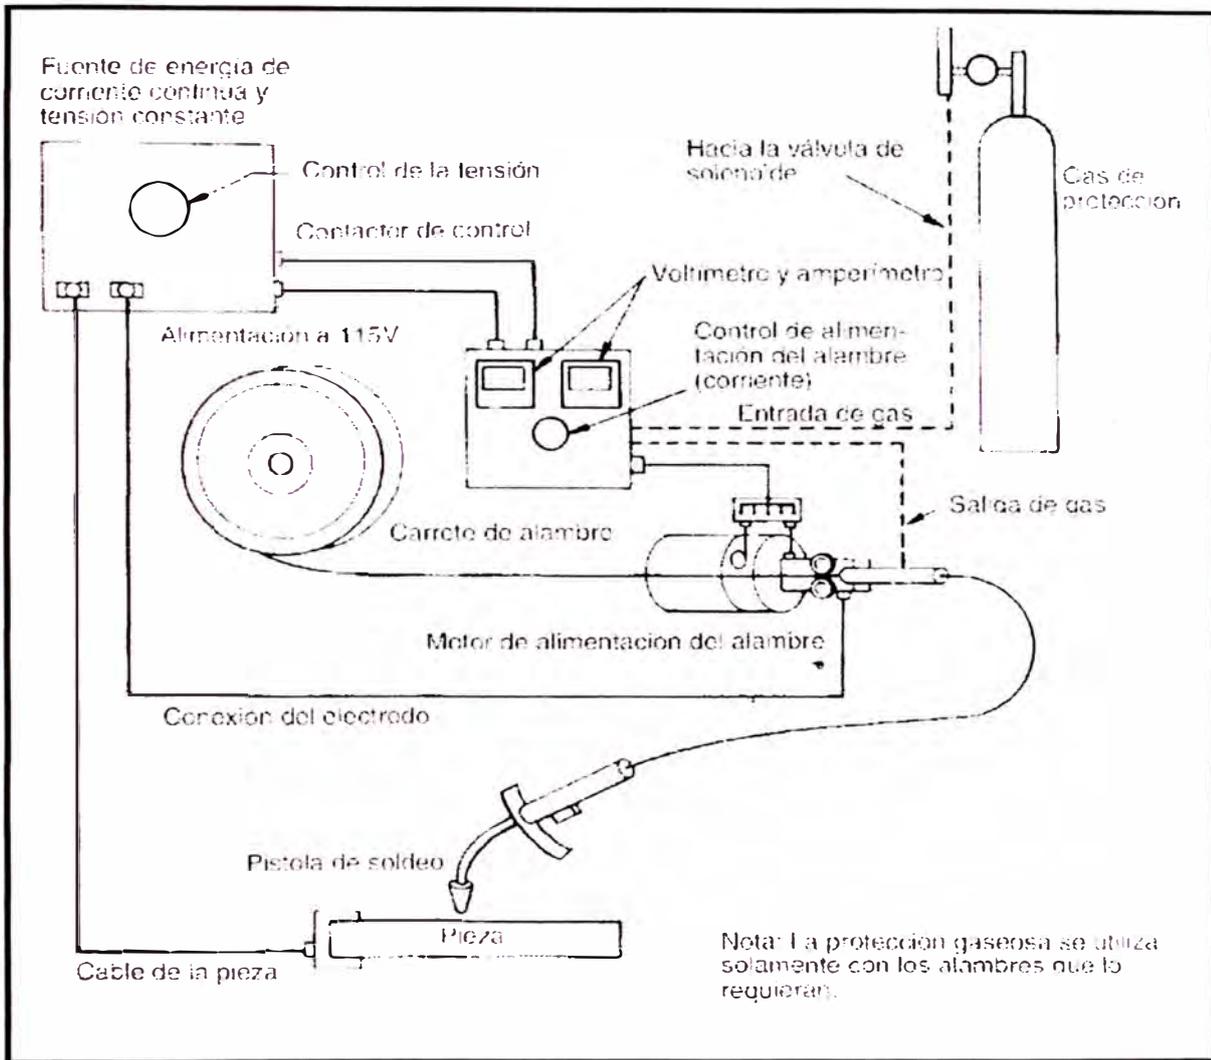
Equipo para el Soldeo por Arco con Alambre Tubular
